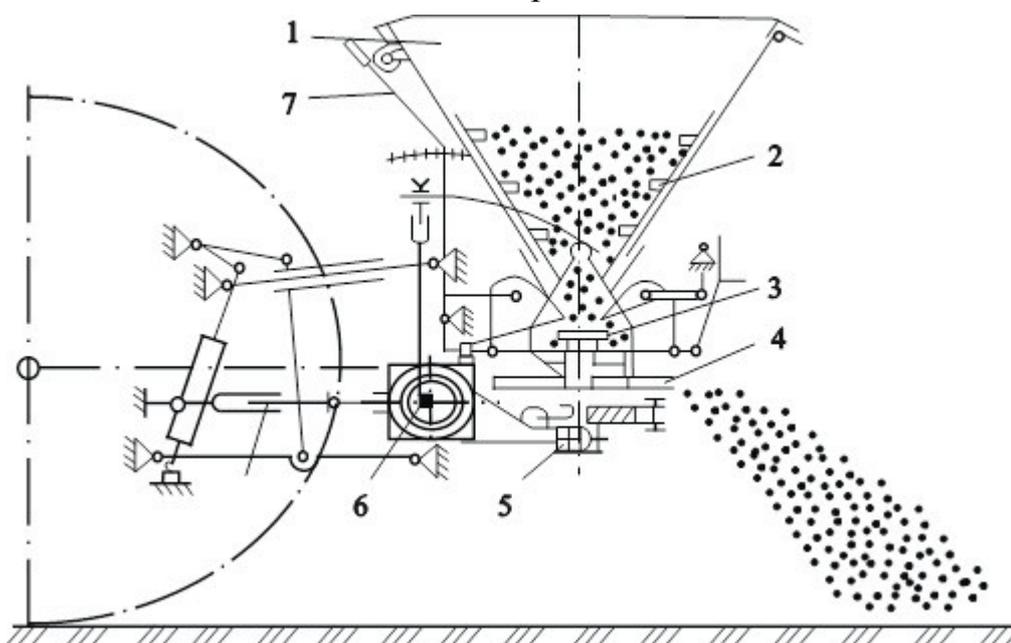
Схема навесного разбрасывателя удобрений МВУ-0,5А: 1 — бункер; 2 — сводоразрушитель; 3 — дозирующее устройство; 4 — разбрасывающий диск; 5, 6 — редукторы; 7 — регулятор
